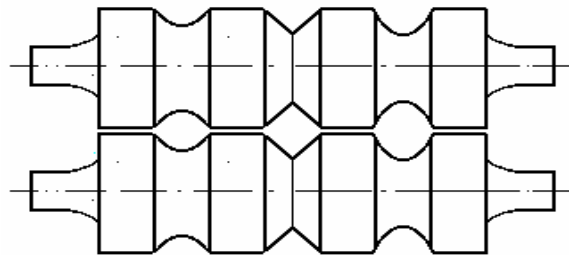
Desenho de um par de cilindros de laminação com canais usinados
